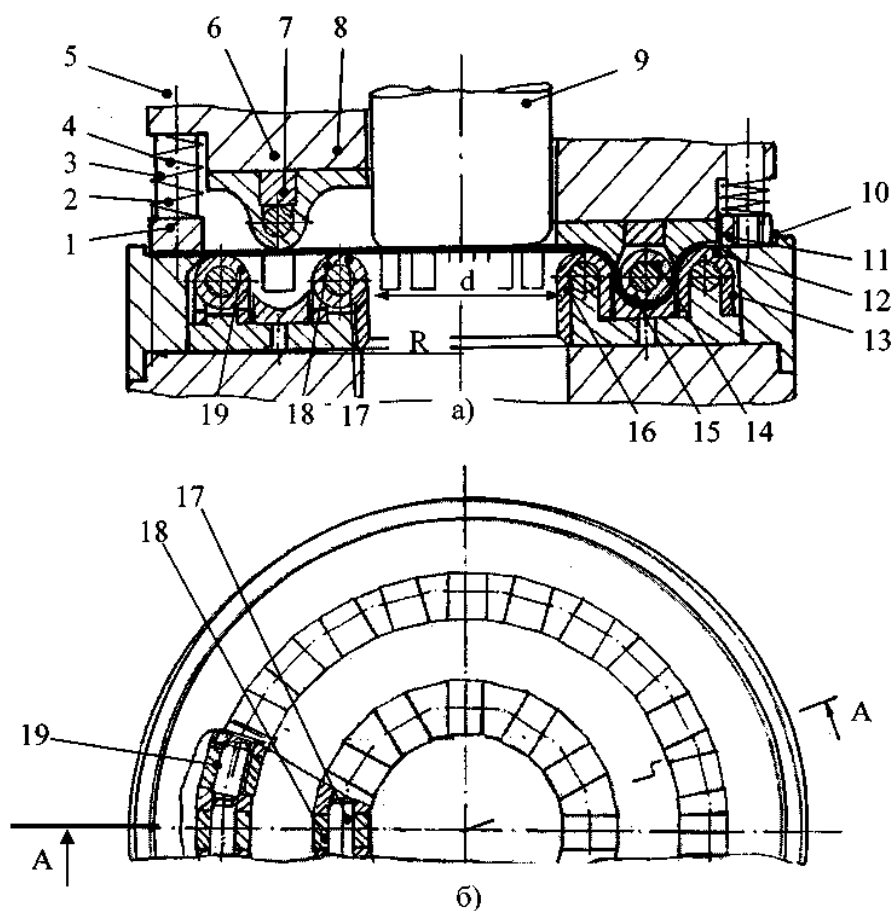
Продольный разрез штампа для глубокой вытяжки:
